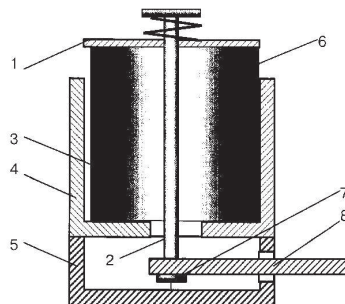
Конструктивная схема резинового виброизолятора подвесного типа: 1–крышка; 2–стержень; 3–зазор; 4–кожух; 5–корпус; 6–резиновый упругий элемент; 7–головка стержня; 8–кронштейн для крепления к опорной поверхности станка.
